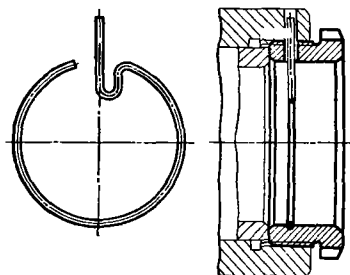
Стопорение гайки пружинным разрезным кольцом
